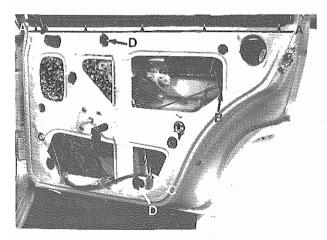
A - Viti fissaggio raschia acqua cristalli Water scraper fixing screws
